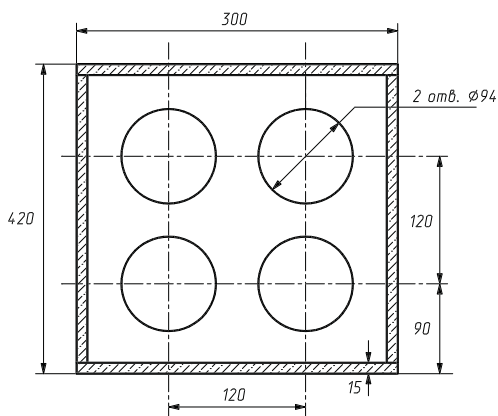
Корпус громкоговорителя без задней стенки с четырьмя головками
